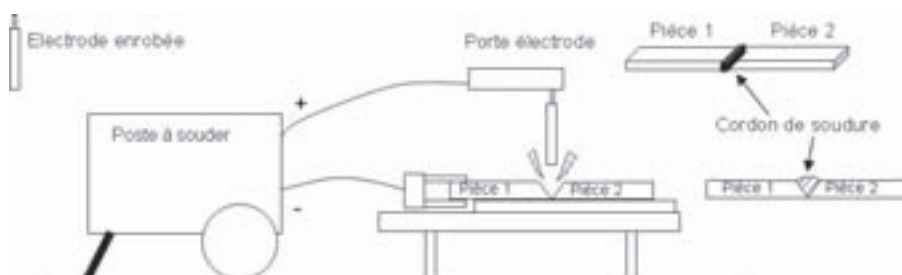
Soudage à l'électrode enrobée.
